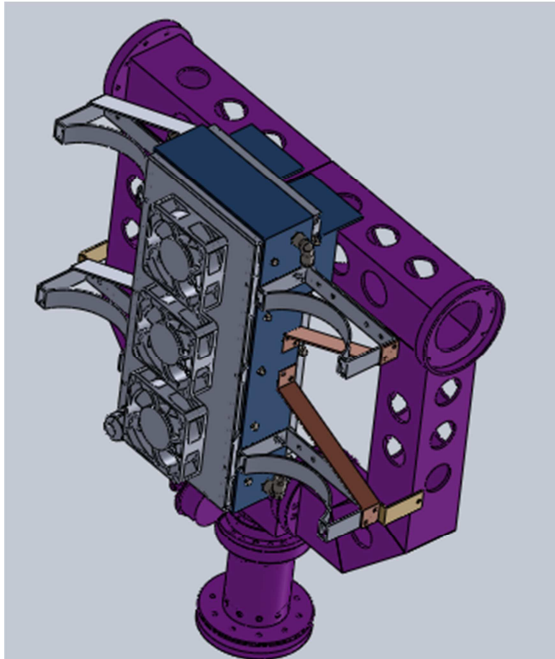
Detalle de la separación entre la pila y la estructura principal
